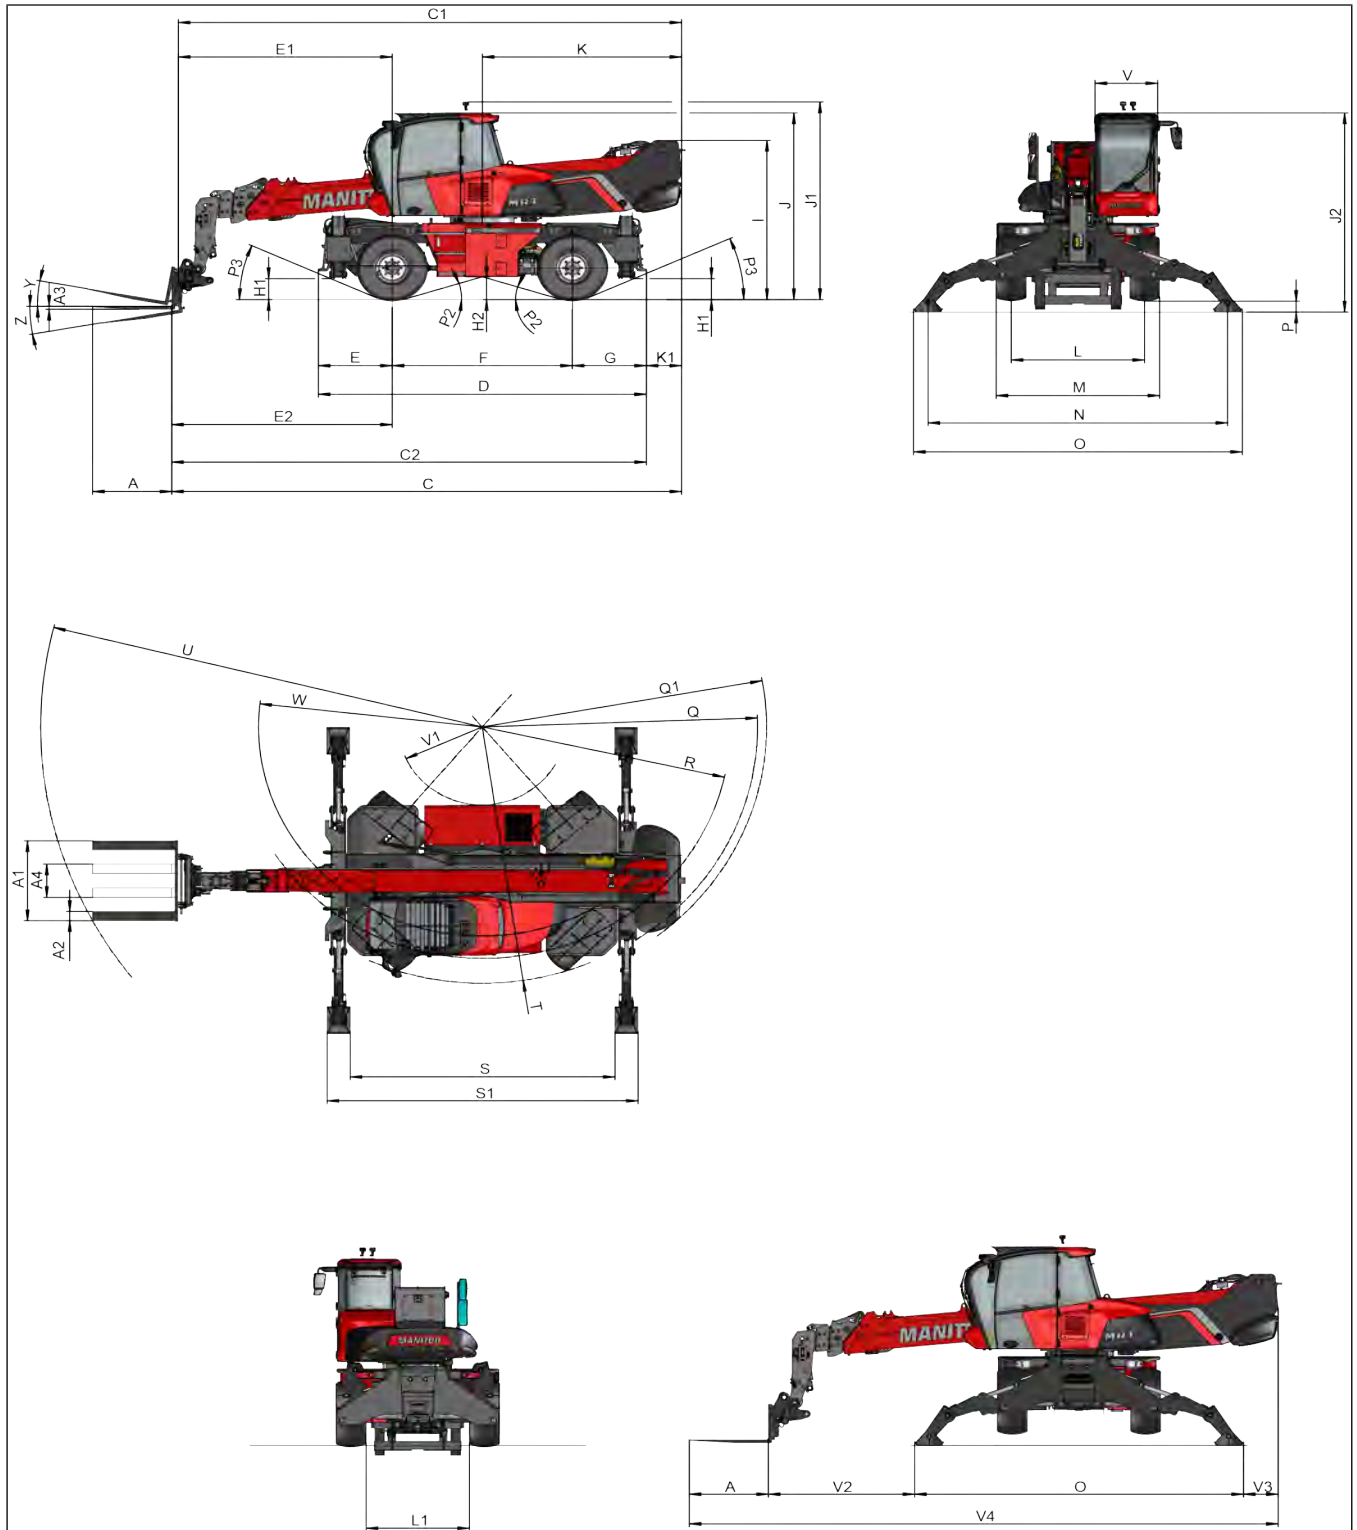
Dimensions (vue latérale, vue de face et vue de dessus)
